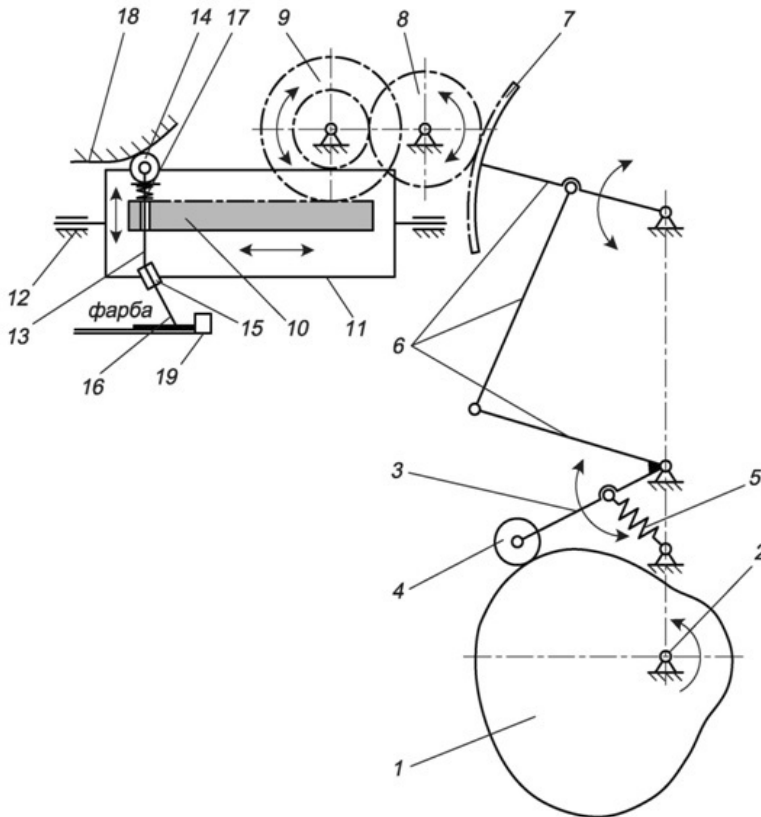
Схема ракульного пристрою для верстатів трафаретного друку: 1 — кулачок, 2 — вал, 3 — коромисло, 4 — ролик, 5 — пружина, 6 — двокоромисловий чотириланковий механізм, 7 — зубчастий сектор, 8 — зубчаста шестерня, 9 — зубчасте колесо, 10 — зубчаста рейка, 11 — каретка, 12 — нерухомі напрямні, 13 — двоплечий важіль, 14 — ролик, 15 — ракелетримач, 16 — ракуль, 17 — пружина, 18 — нерухома гірка, 19 — друкарська форма
